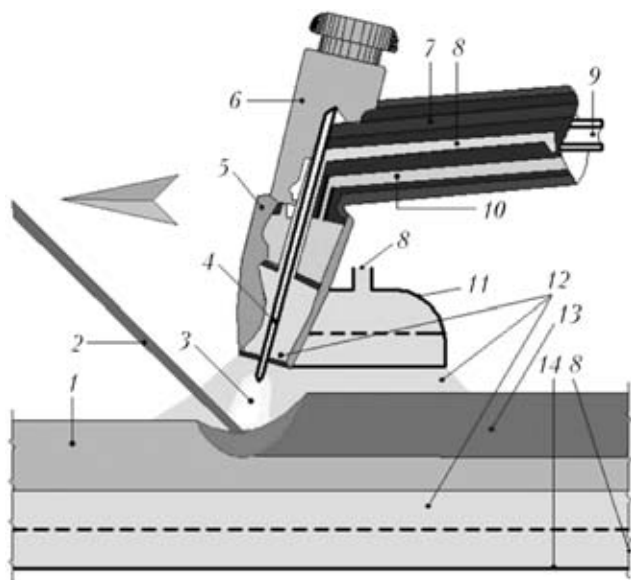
Схема ручной сварки ТИГ титана: 1 — свариваемый металл; 2 — присадочная проволока; 3 — дуга; 4 — неплавящийся электрод; 5 — сопло; 6 — корпус горелки; 7 — подача охлаждающей воды; 8 — подача защитного газа; 9 — токоподвод; 10 — отвод воды; 11 — насадка для защиты остывающих участков шва; 12 — защитная среда; 13 — металл шва; 14 — приспособление для защиты обратной стороны шва
